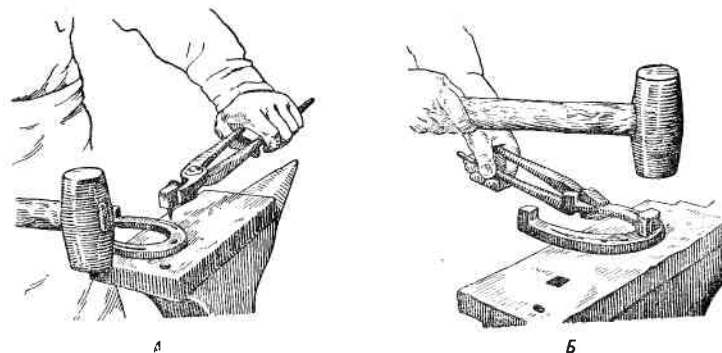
Укрепление зацепного шипа для сварки:
